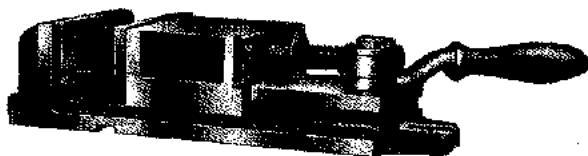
Tornillo de mordazas corriente (Cincinnati Milling Machine Co.)
